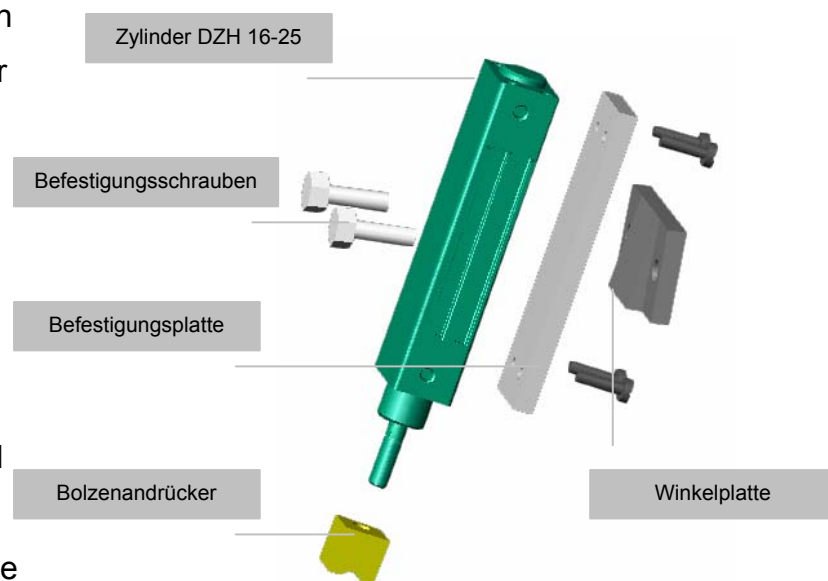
Bolzenfixierung in Explosionsansicht
